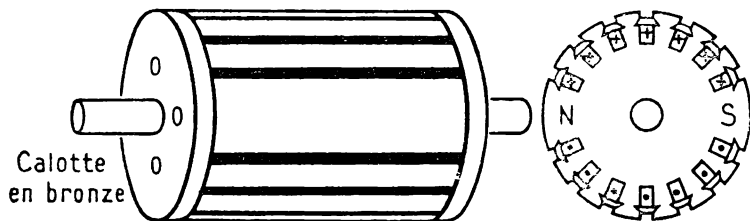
Rotor lisse d'un turbo-alternateur.
